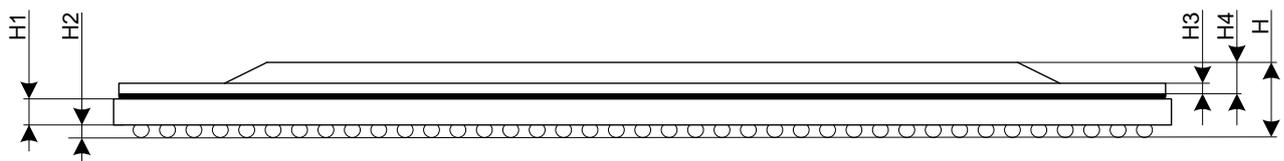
Корпус микропроцессора BE-M1000 (вид сбоку)
